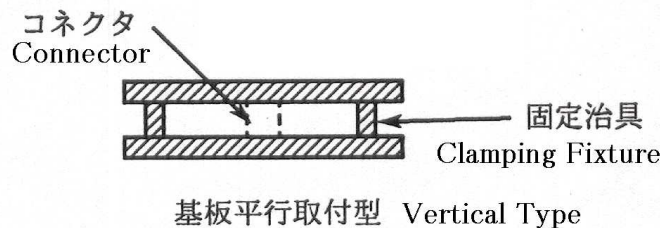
コネクタ固定方法 / Method of Connector Mounting for Vibration and Hammering Shock
